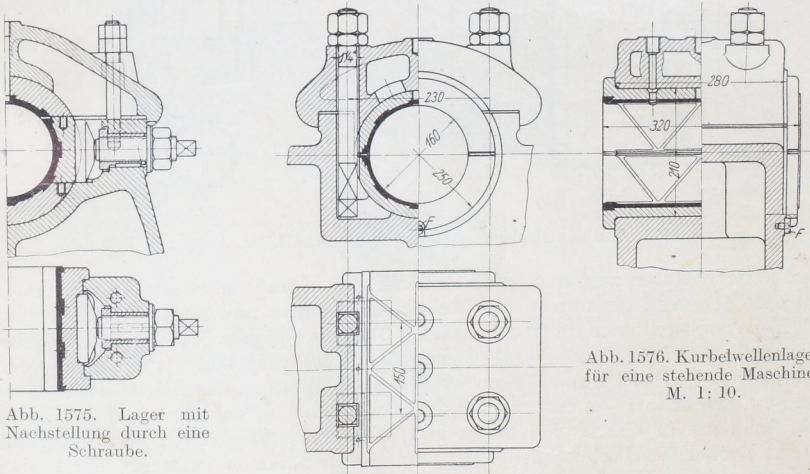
Kurbelwellenlager für eine stehende Maschine.
